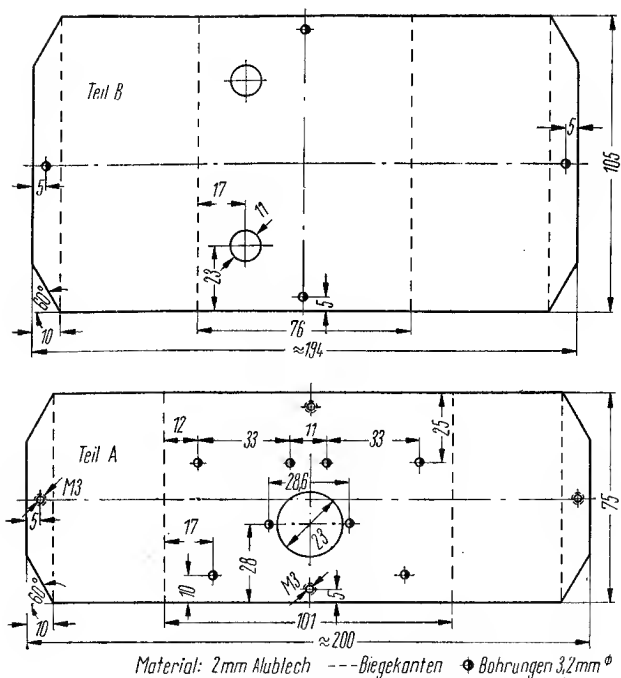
Maßskizze für das Chassis des KW-Kanverters
